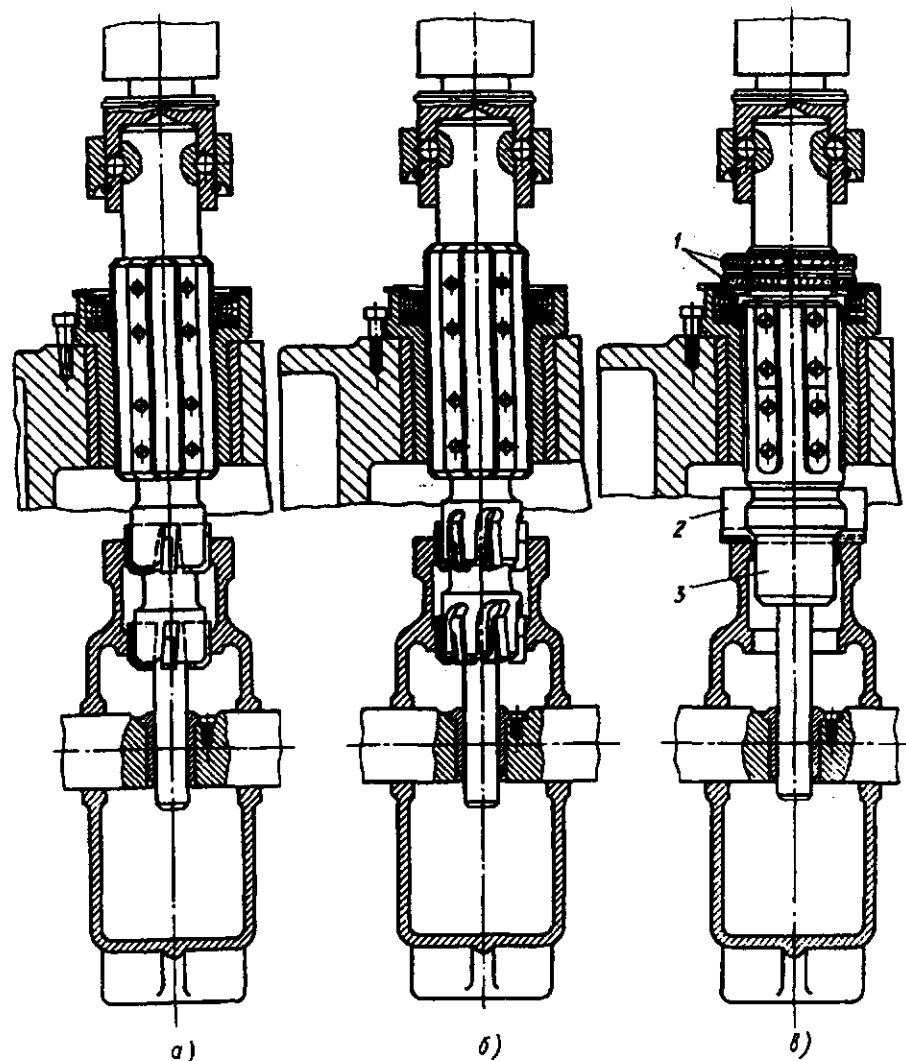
Схемы последовательной обработки в корпусе двух отверстий на радиально-сверлильном станке: а - черновое и полуступенчатое зенкерование двух отверстий "в линию"; б - развертывание двух отверстий "в линию"; в - подрезание фланца
